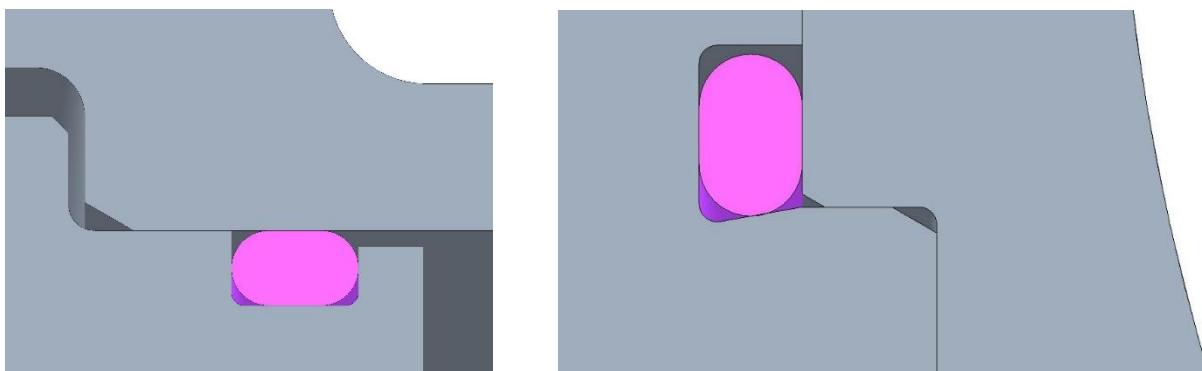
Detailní pohled na spojení obou polovin spojky
